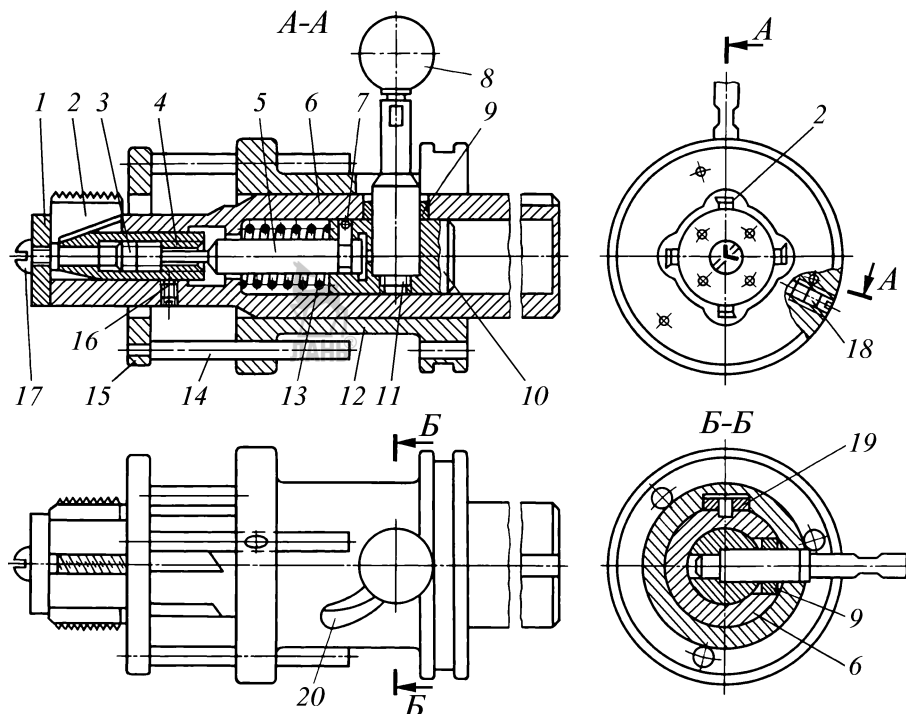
Невращающаяся головка для нарезания внутренней резьбы:
